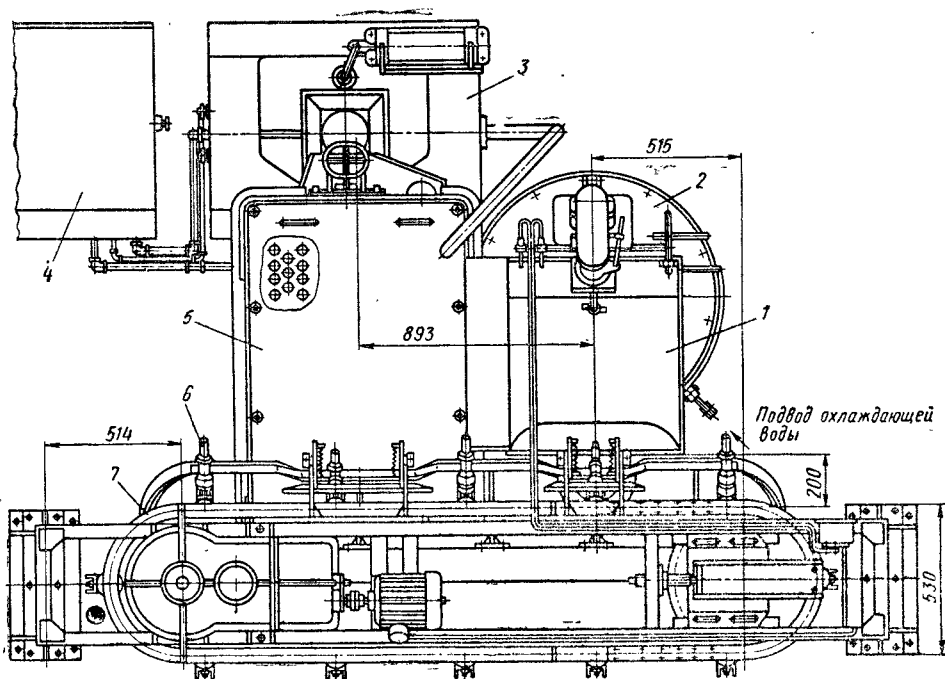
Полуавтоматическая установка НИИТАвтомпрома и ЗИЛа для обмазки и обсыпки модельных блоков:
